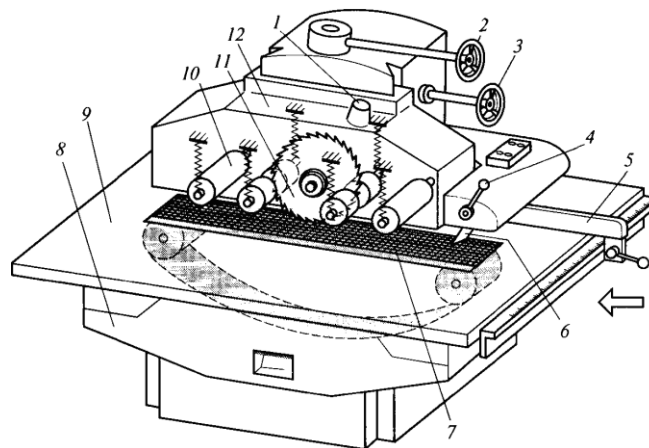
Однопилковий прирізний верстат з конвеєрною подачею: 1 – патрубок; 2 – маховичок настроювання притискного супорта; 3 – маховичок настроювання пильного супорта; 4 – рукоятка підйому кігтевого захисту; 5 – напрямна лінійка; 6 – кігтевий захист (хитний упор); 7 – конвеєр; 8 – станина; 9 – стіл; 10 – притискний ролик; 11 – пилка; 12 – супорт притискних роликів
